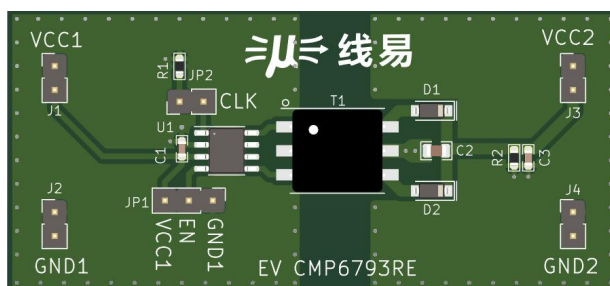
PCB 示意图(尺寸: 30x 65mm)
